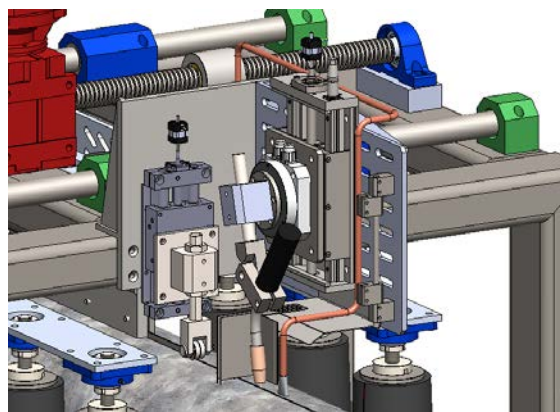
Posicionamento do mecanismo de soldadura
